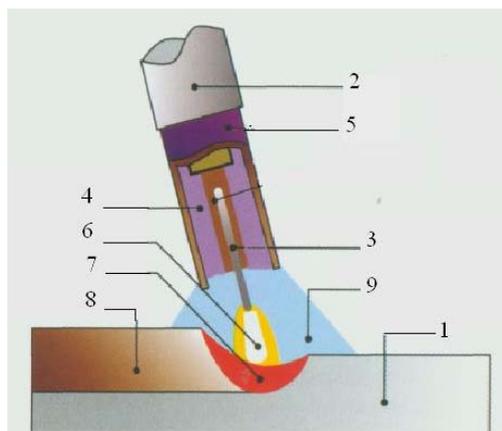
Схема процесса наплавки электродной проволокой в среде аргона: 1 – наплавляемое изделие; 2 – горелка; 3 – электродная проволока; 4 – защитный газ; 5 – газовое сопло; 6 – сварочная дуга; 7 – сварочная ванна; 8 – наплавленный валик; 9 – защитная атмосфера
